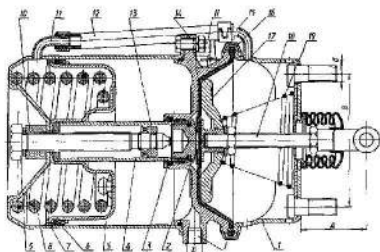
Тормозная камера с пружинным энергоаккумулятором: 1—корпус; 2—толкатель; 3—кольцо уплотнительное; 4—труба; 5—поршень; 6—уплотнитель; 7—цилиндр; 8—пружина; 9—винт; 10—бобышка; 11, 15—патрубки; 12—шланг; 13—упорное кольцо; 14—фланец; 16—мембрана; 17—диск; 18—шток; 19—возвратная пружина. I—подвод сжатого воздуха в рабочую камеру, II—подвод в пружинный энергоаккумулятор
